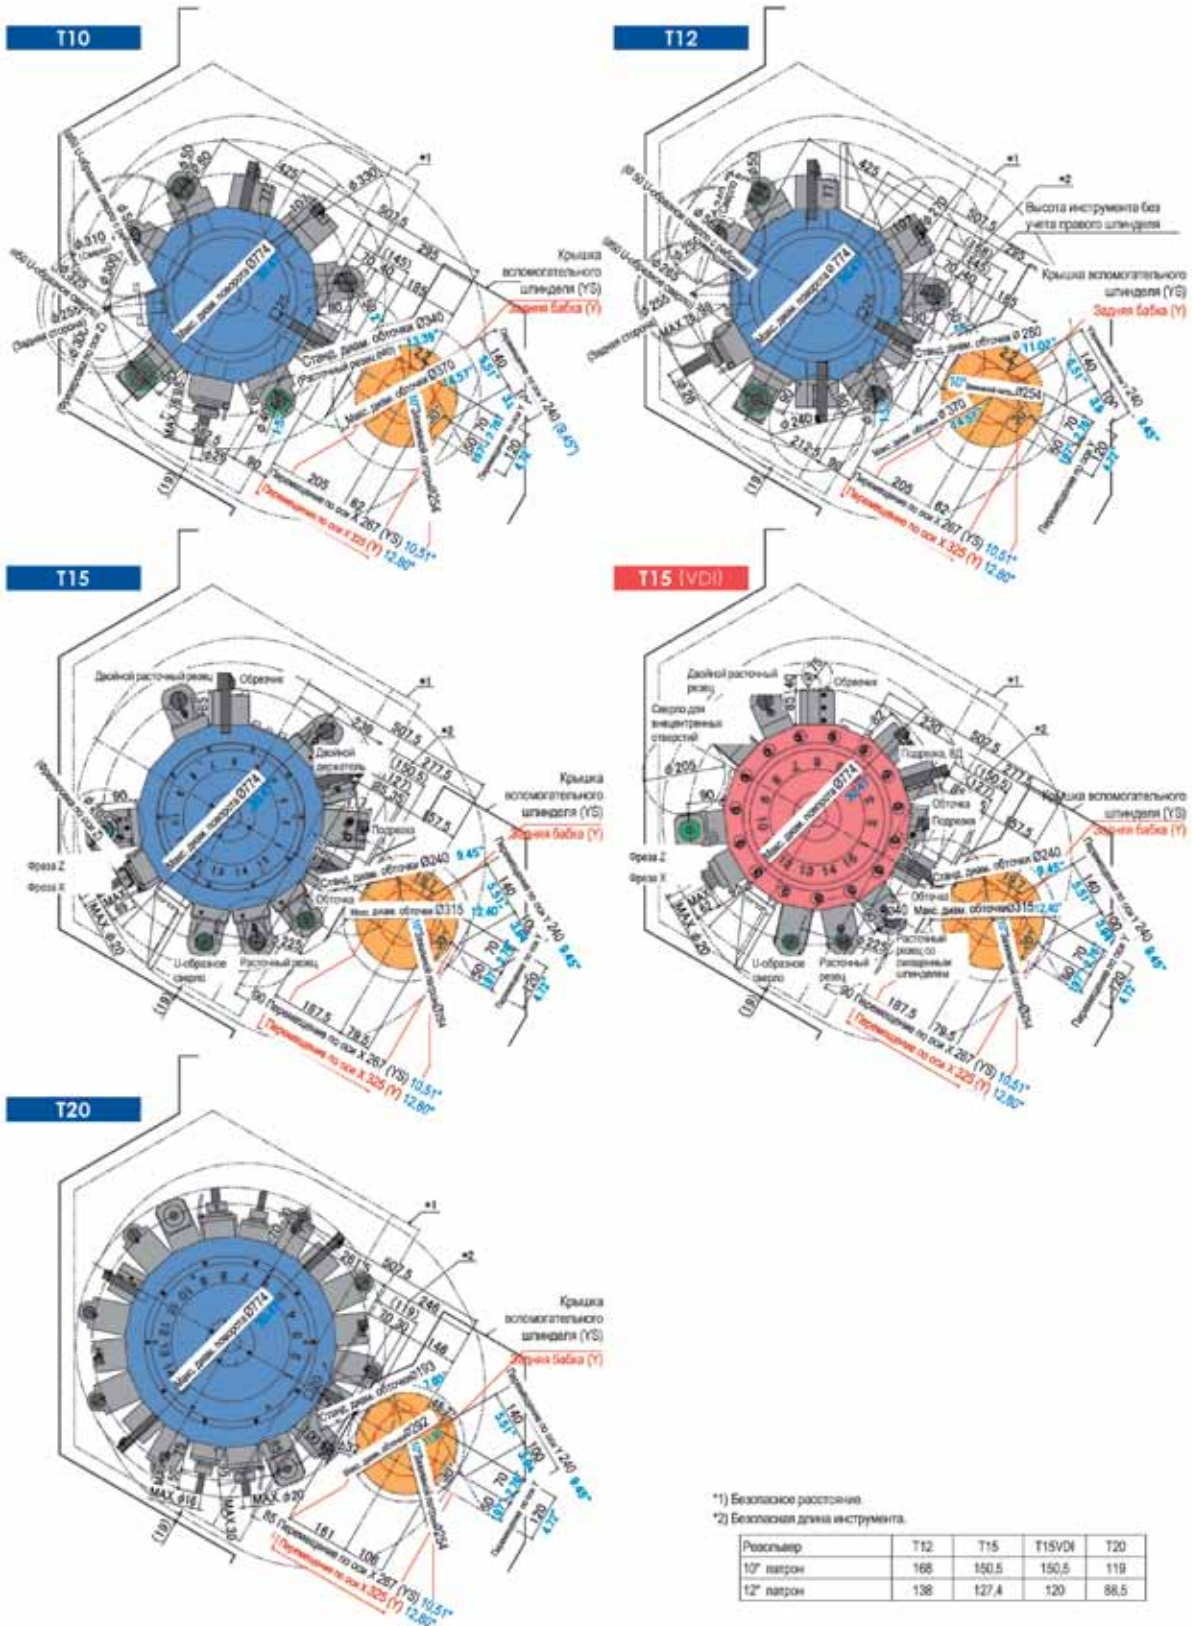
Стандартный/максимальный диаметр обточки 280/370 (T12)
